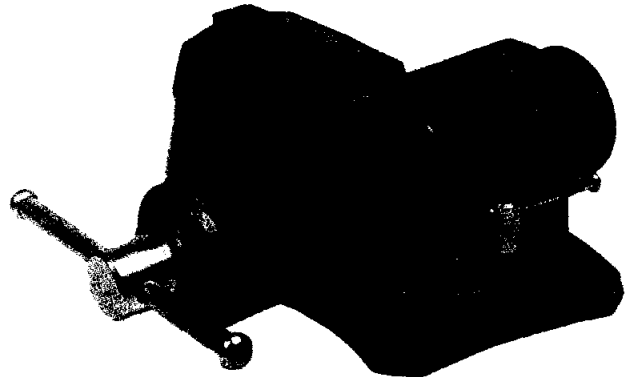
Tornillo de banco (cortesía de Imporhesur).
